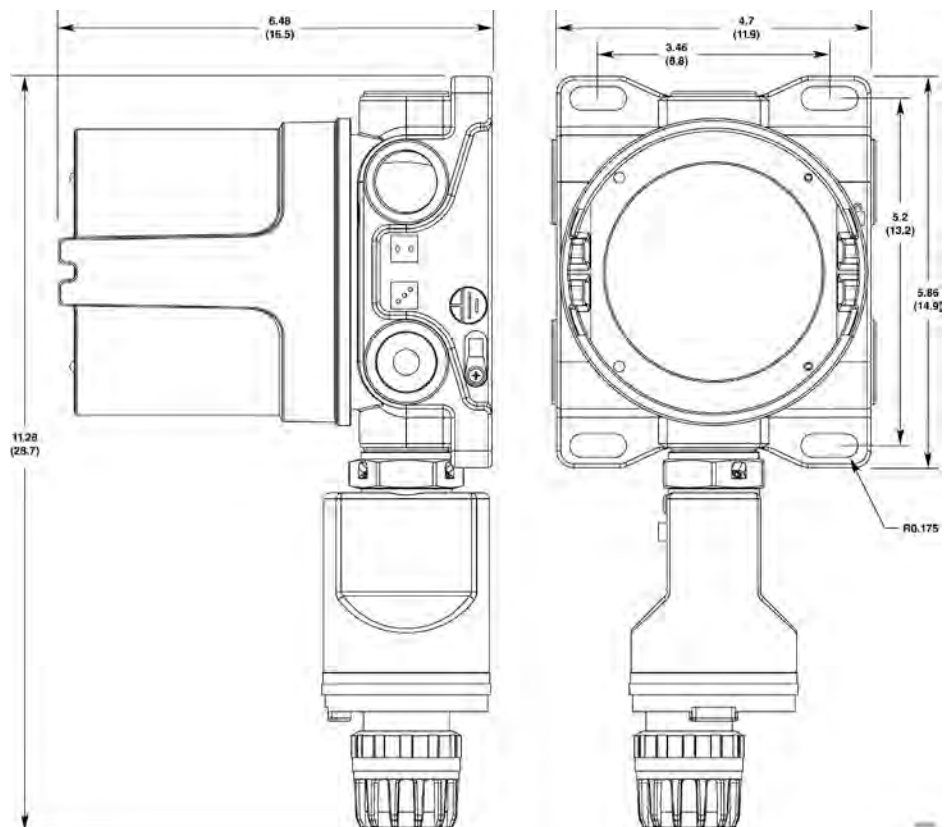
Габаритные и установочные размеры контроллера с газоанализатором GT3000 в дюймах (сантиметрах).
